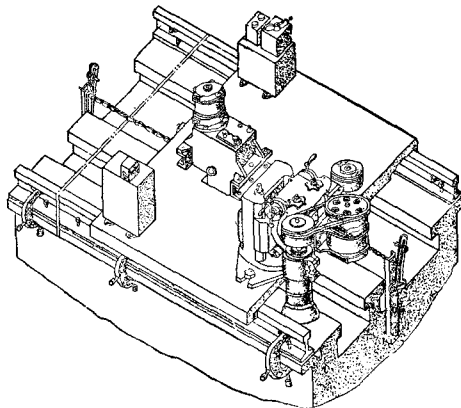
Базирование приспособления для обработки направляющих по вершинам призматических направляющих: 1 и 2 — поверхности, на которых базируется приспособление.
